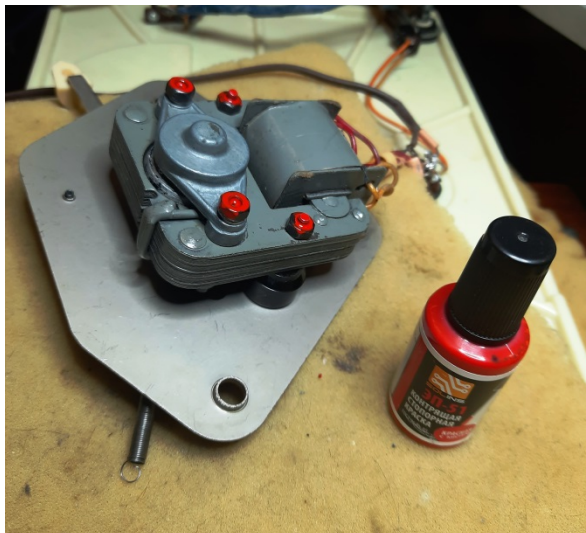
Двигатель после смазки, центровки и сборки. Все винты законтрены эмалью ЭП-51.
